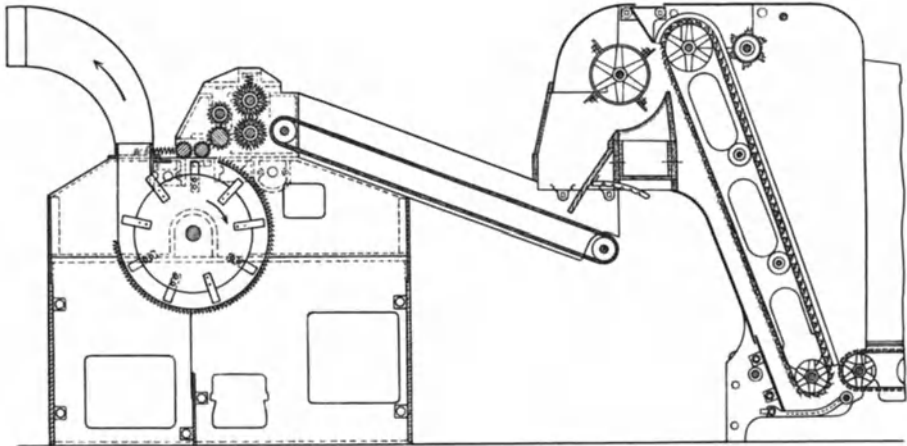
Horizontalöffner mit Buckley-Schläger, Lattentuchzuführung und Kastenspeiser (Saco-Lowell, Boston).
